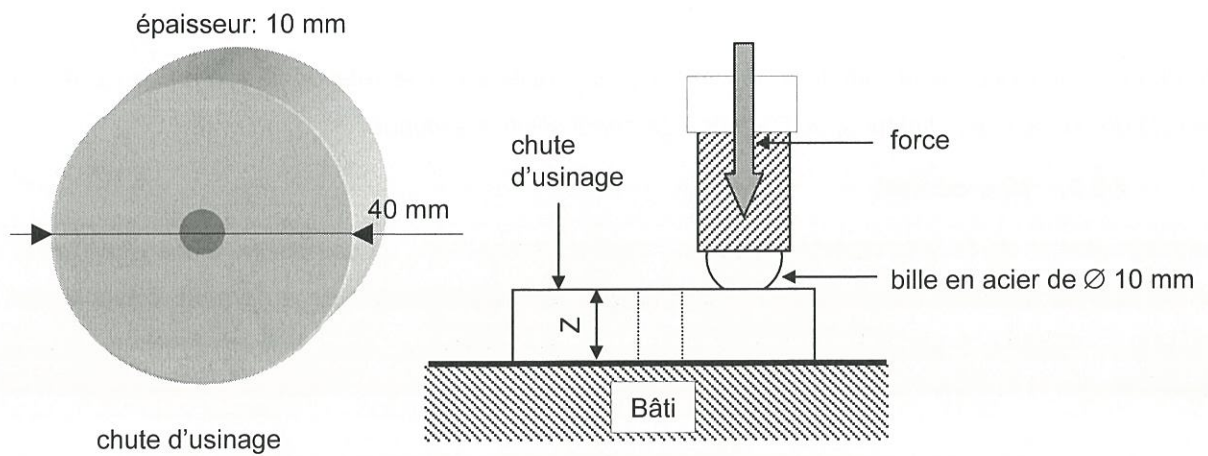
schéma du montage employé pour la mesure de la macrodureté et géométrie des éprouvettes
